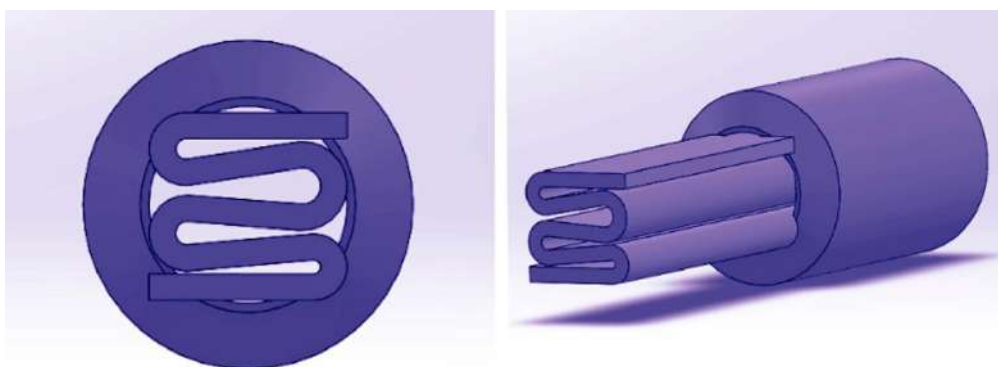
Токоподвод для размерной обработки поверхности металлов в виде “гармошки” для работы при ($Gv = 28-90$ л/ч)
